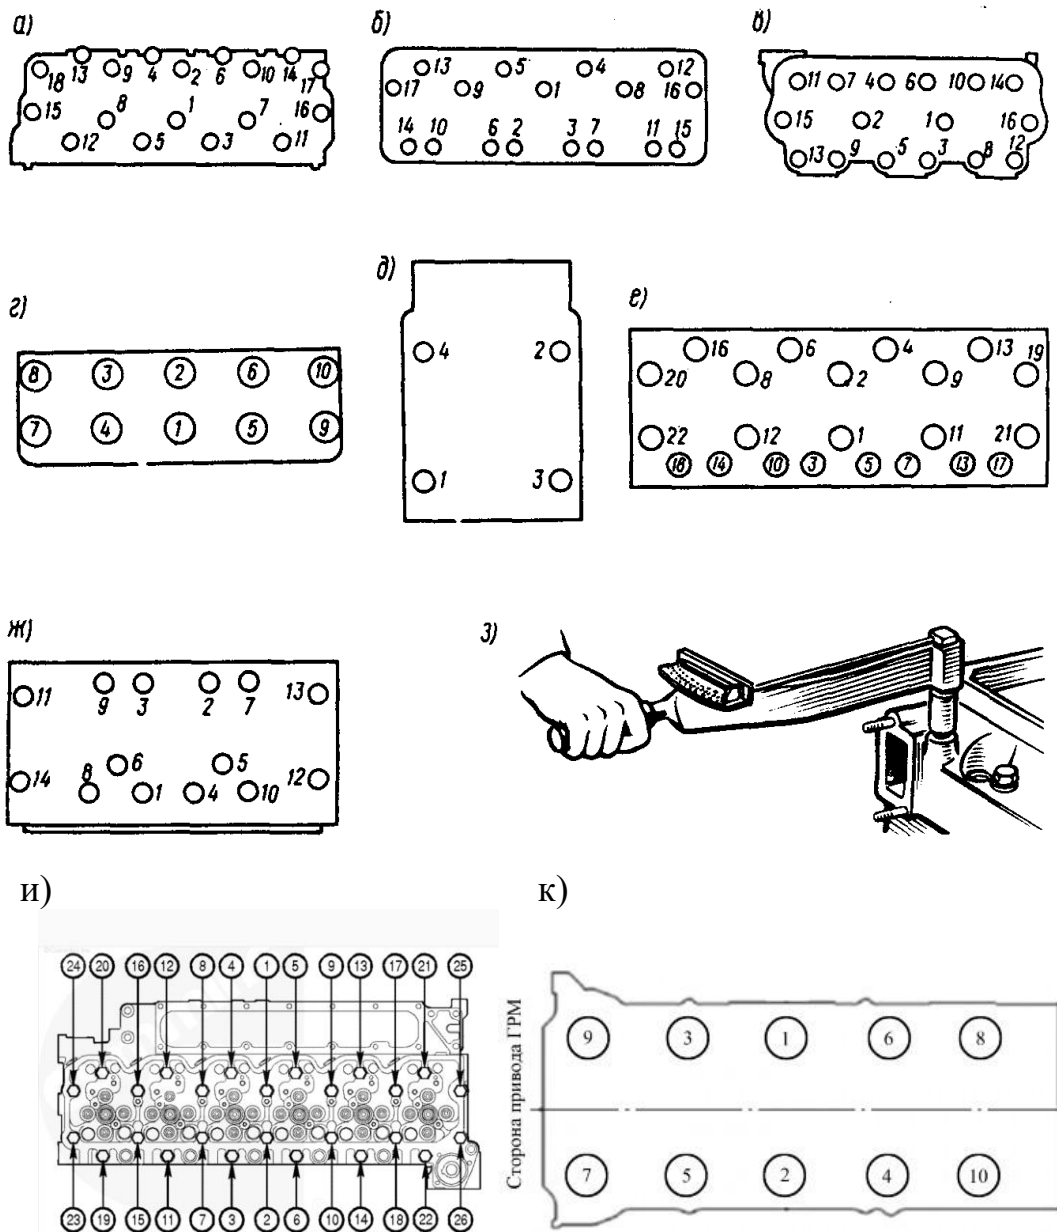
Порядок затяжки болтов (гаек) крепления головки блока цилиндров двигателей автомобилей: а – ГАЗ-53-12; 66-11; -14 «Чайка»; б – ЗИЛ-130, Урал-375Д, автобусы ЛиАЗ-677, ЛАЗ-695Н, – 699Р; в – МАЗ-5335; г – ГАЗ-3102 «Волга»; д – КАМАЗ-5320; е – ЗИЛ-4331; ж – Икарус-260; з – торцовый ключ с динамометрической рукояткой; и – КАМАЗ-65115 cummins двигатель bisbe285; к – ВАЗ (LADA) XRAY 1.6 MT.
